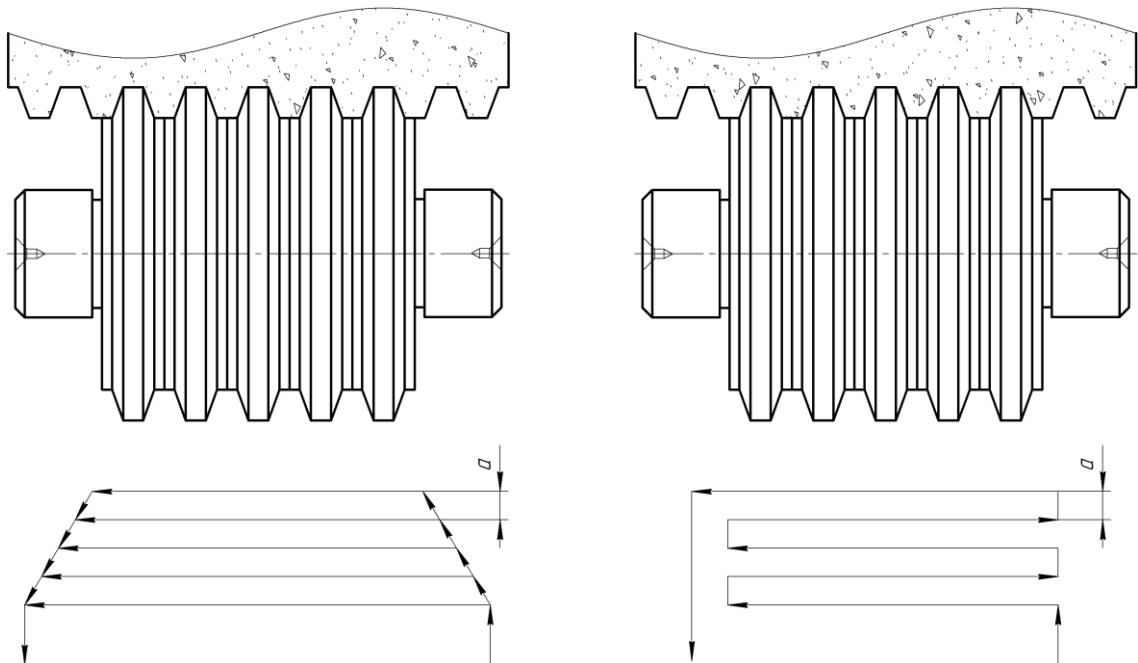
Схемы накатки червячной поверхности гиперболоидного шлифовального круга: а) односторонняя; б) двухсторонняя
